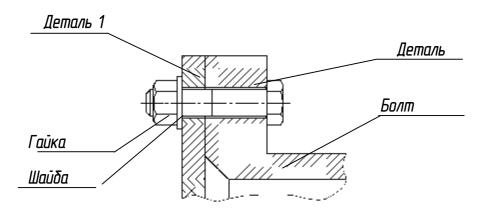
Резьбовое соединение, в котором применены болт, гайка и шайба
